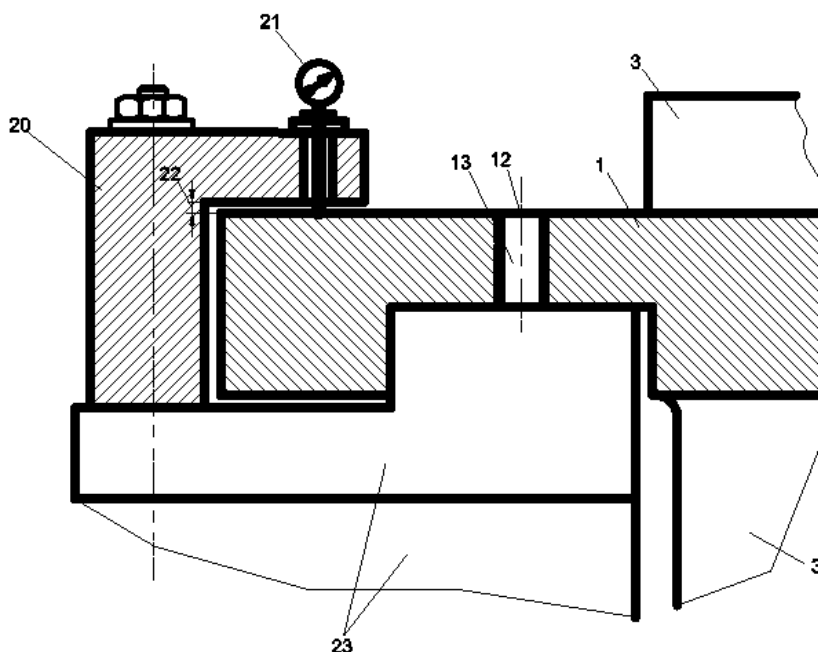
Схема расположения отверстия под рым-болты и установки измерителя подъема лап:
